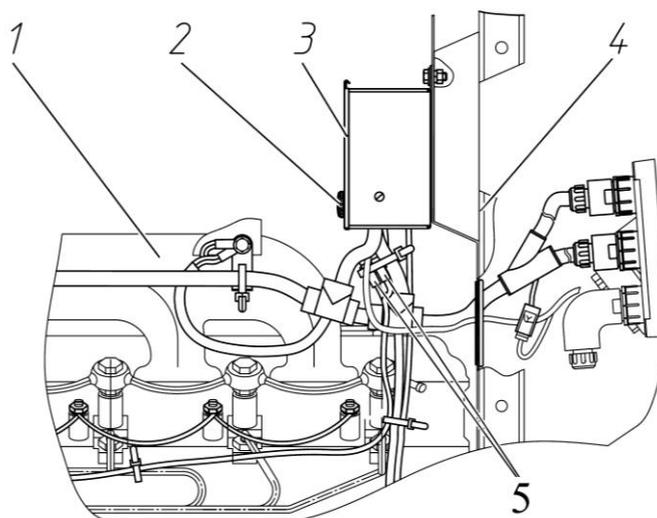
Доступ к предохранителям, расположенным на раме крепления облицовки
